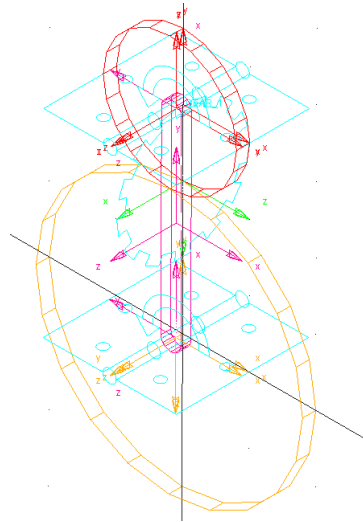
Representación de un engranaje (*gear*) en *ADAMS View
